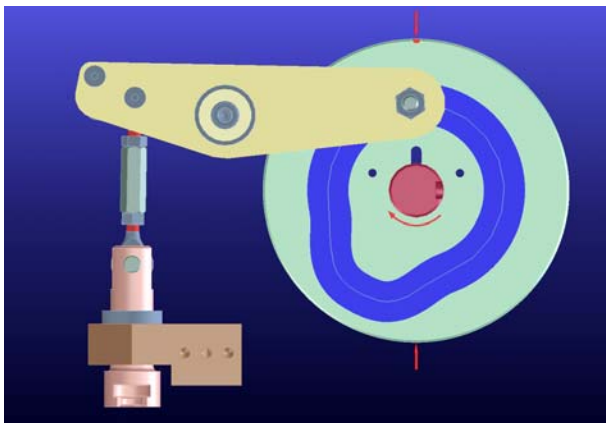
Schubkurbel mit Nutkurve für Schnittwerkzeugbewegung
